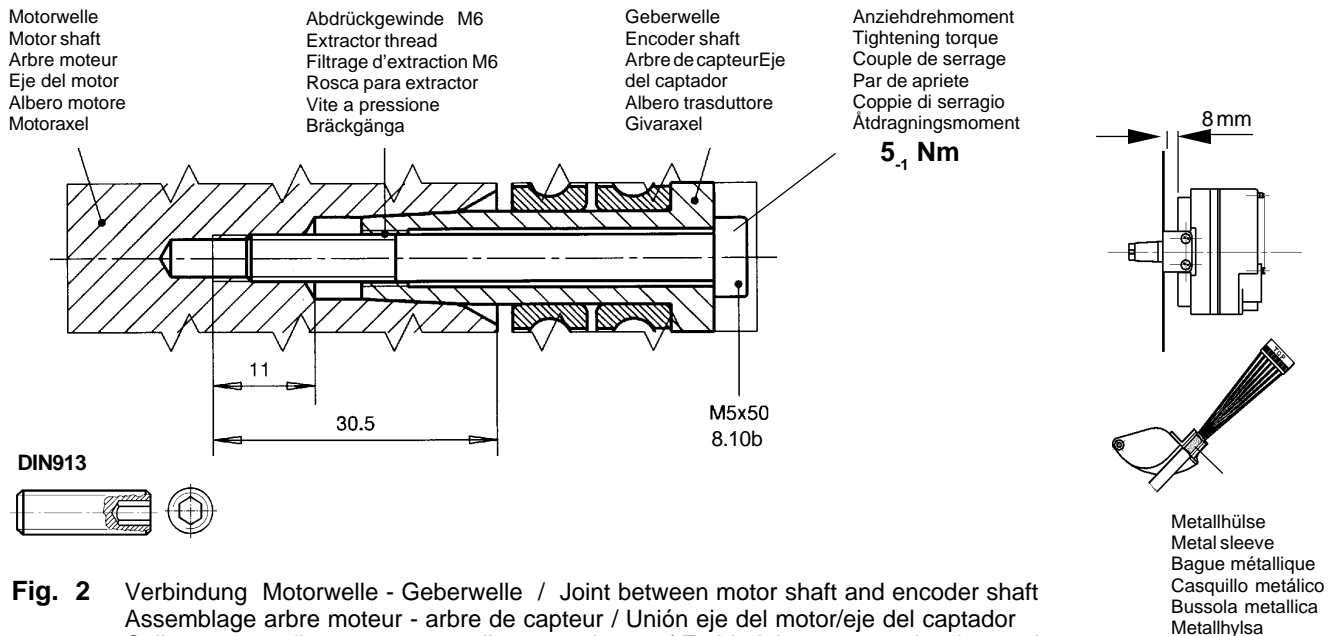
Verbindung Motorwelle - Geberwelle / Joint between motor shaft and encoder shaft
